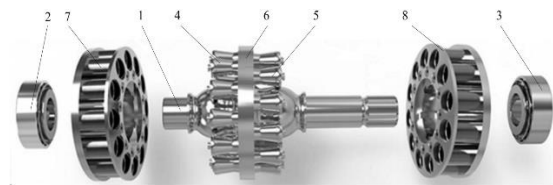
Основні вузли гідромашин Innas з постійним робочим об'ємом: 1 – приводний вал; 2 і 3 – опорні підшипники вала; 4 і 5 – блоки поршнів; 6 – проміжна пластина; 7 і 8 – блоки циліндрів з плаваючими чашками
